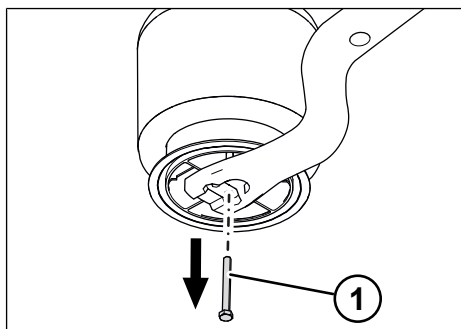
Retirer la vis de fixation de la membrane de suspension pneumatique
